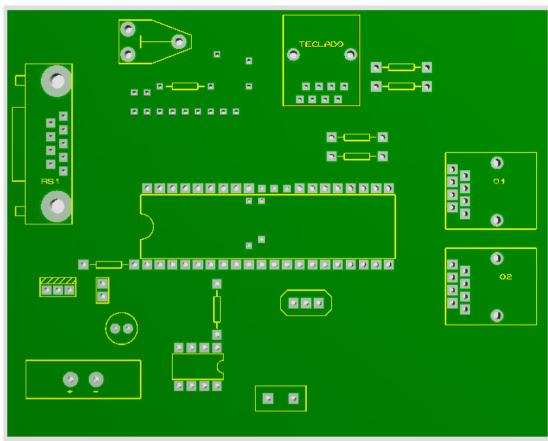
Vista Superior de la tarjeta de acceso en proteus Fuente: Autores
